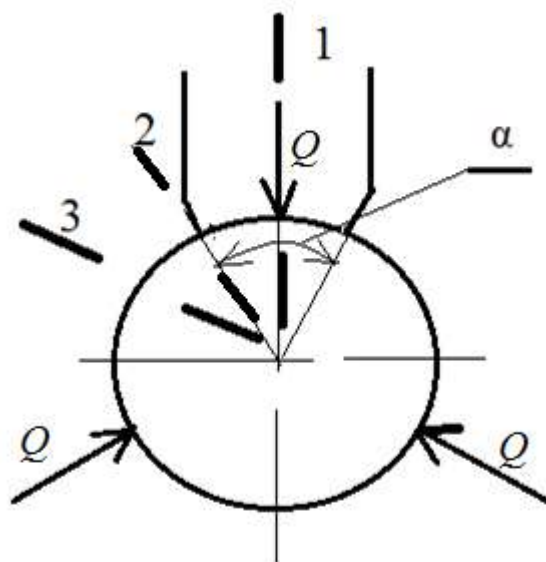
Схема закрепления кольца в широких охватывающих кулачках
